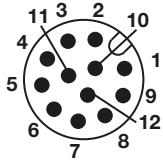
Pinbelegung Stecker M12 (Ansicht Stiftseite)
